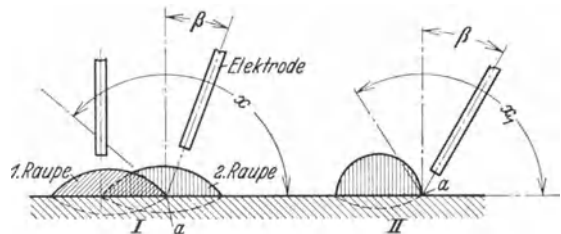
Elektrodenhaltung quer zur Schweißrichtung.
